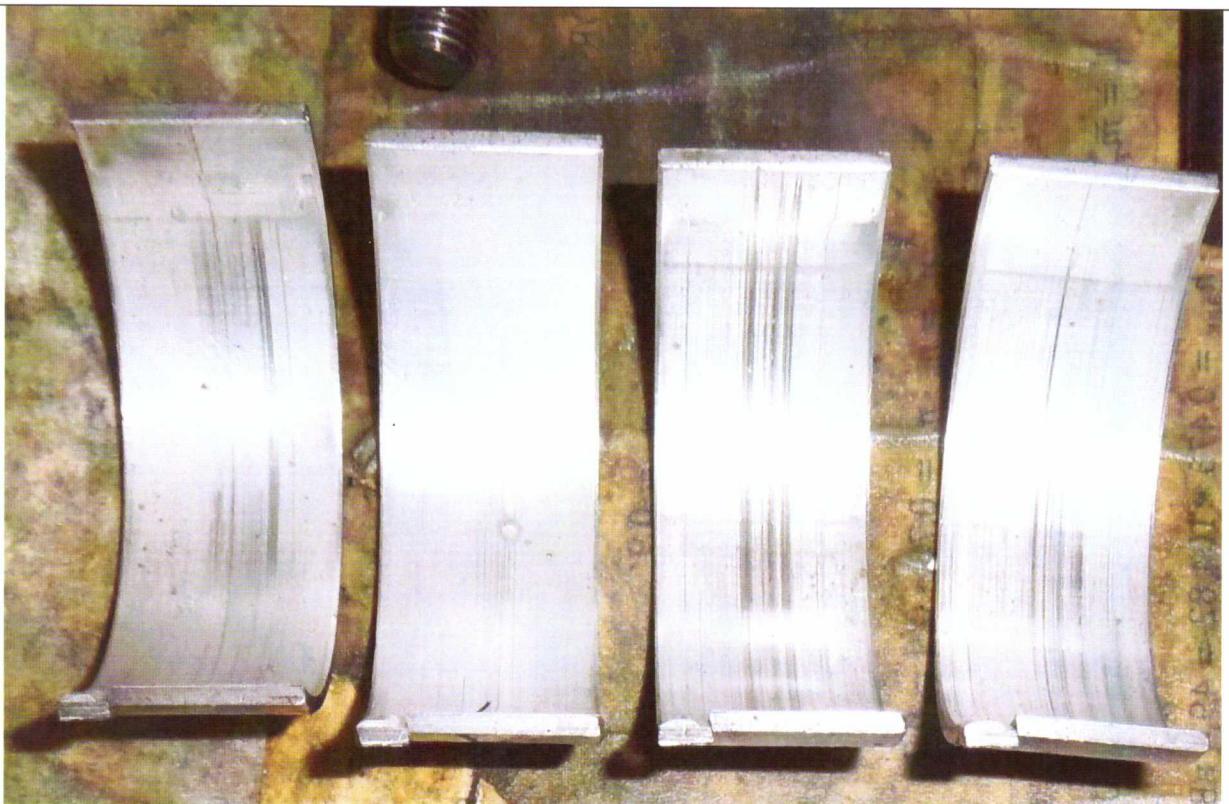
Общий вид рабочих поверхностей верхних вкладышей шатунных подшипников двигателя после аварийного цикла испытаний.
